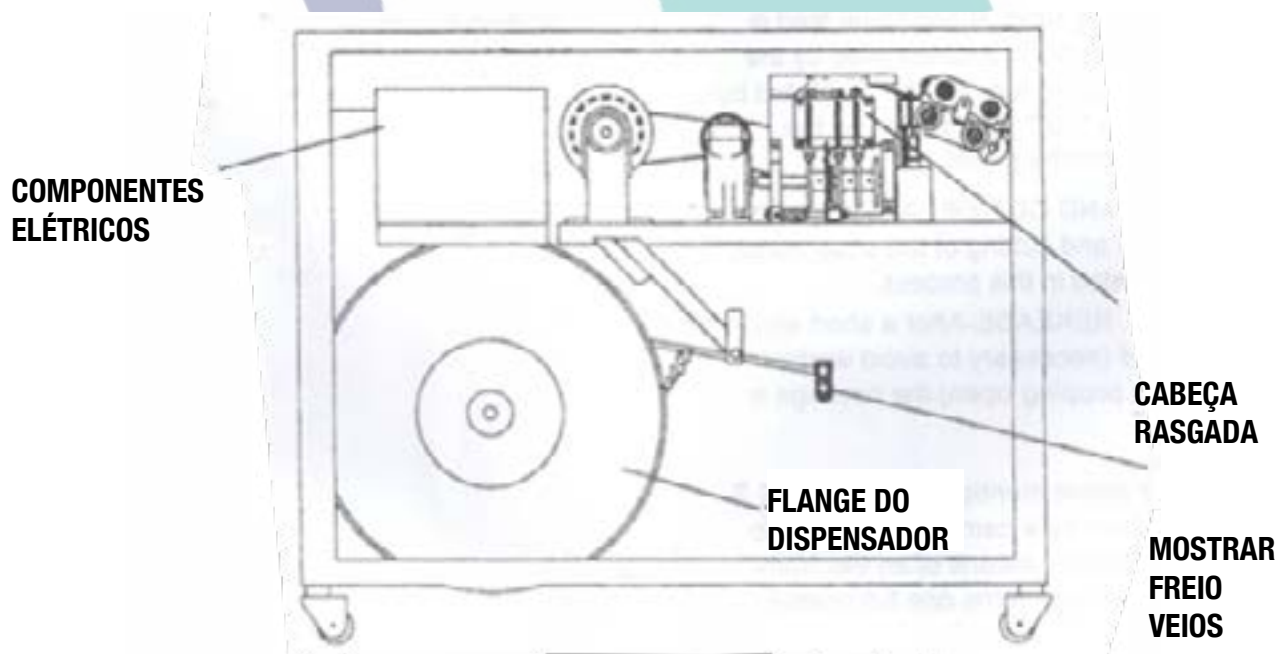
COMPONENTES PRINCIPAIS, VISTAS FRONTAL
